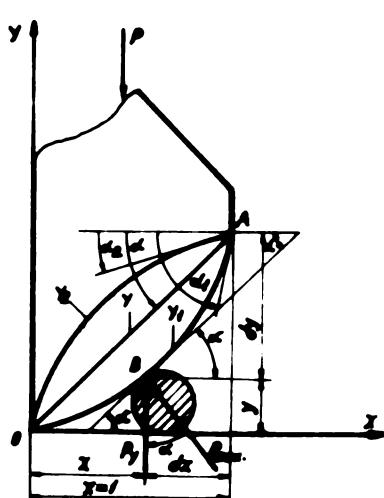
Geometria tăișului cuțitului în plan longitudinal
